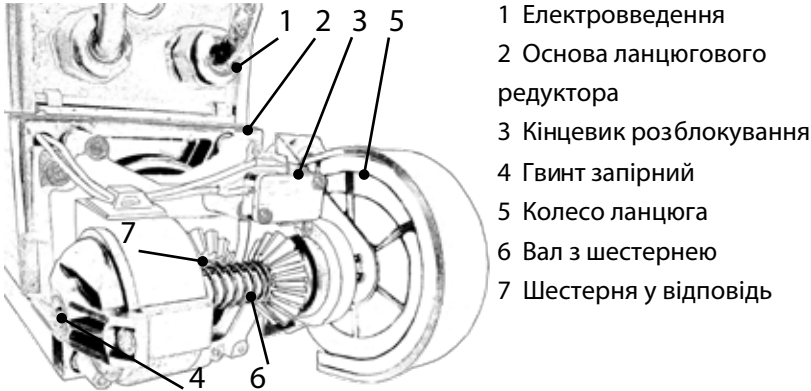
Розміщення ручного ланцюгового редуктора (кришка знята)
